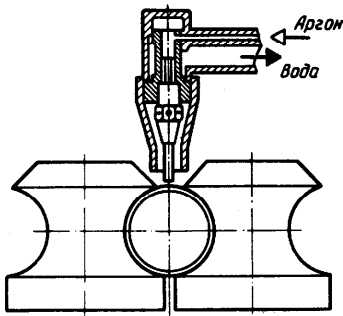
Принципиальная схема аргонодуговой сварки труб
